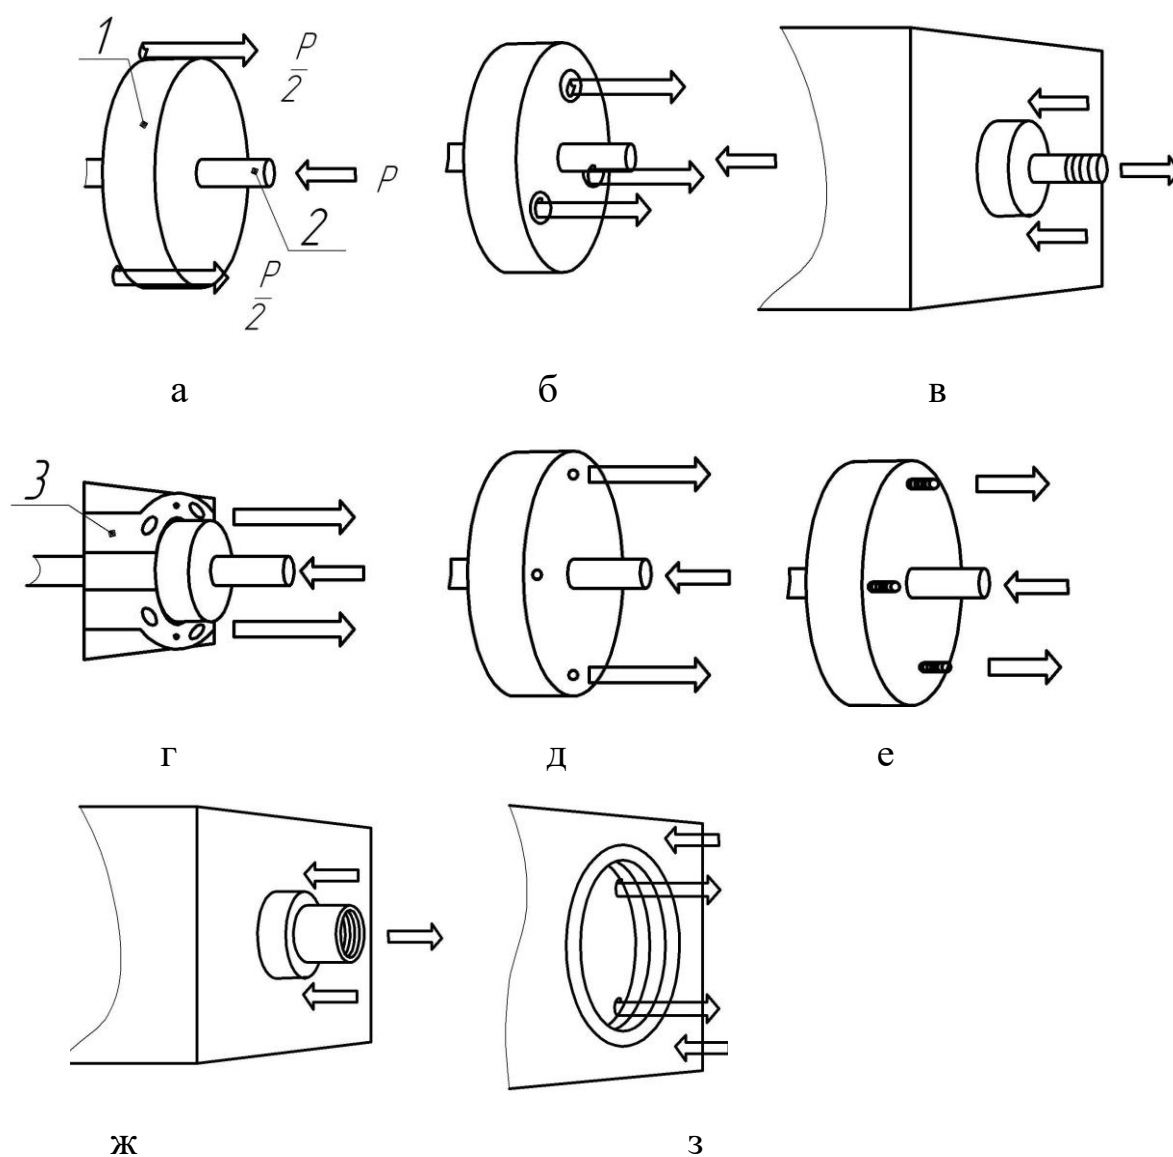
Способы приложения усилия выпрессовки к деталям различной формы: а – з – варианты; 1 – спрессовываемая деталь; 2 – деталь, из которой или с которой спрессовывается деталь; 3 – разъемное устройство
